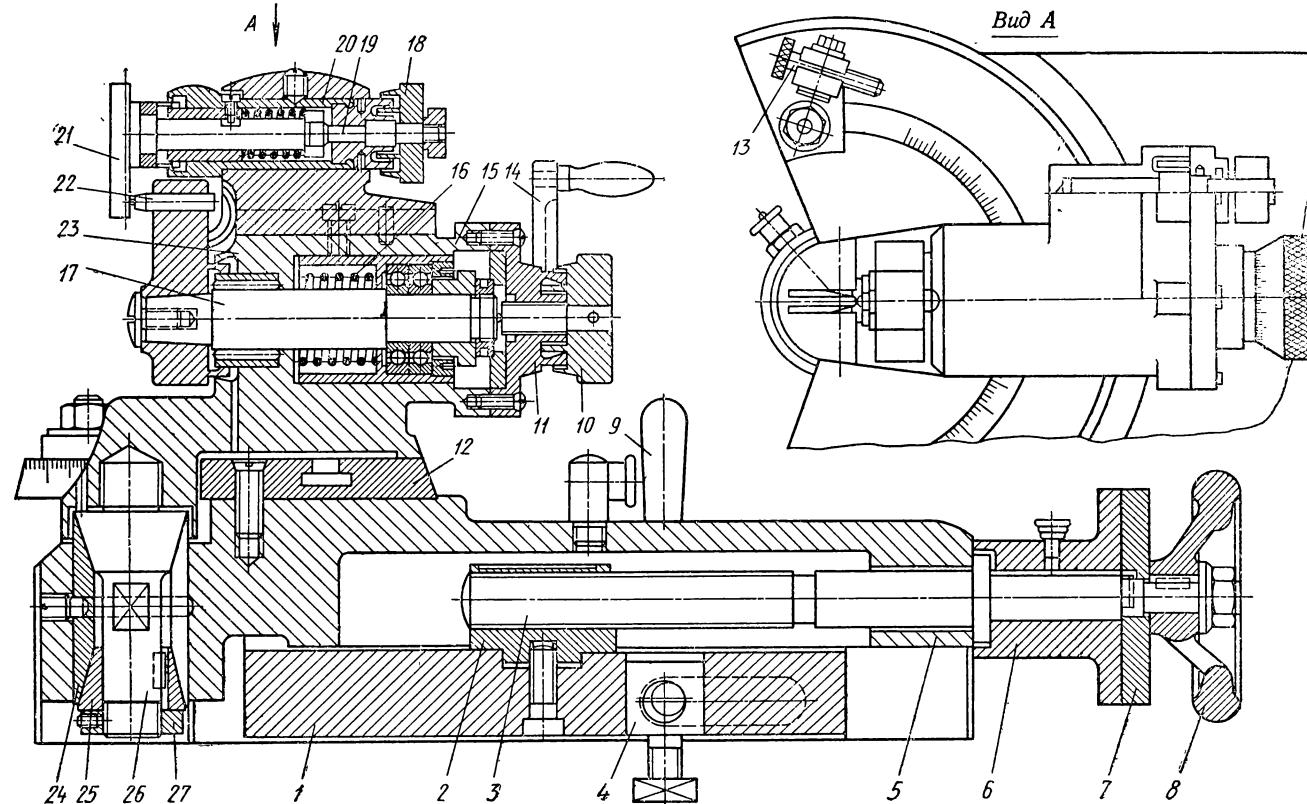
Приспособление к резьбошлифовальному станку для профилирования шлифовального круга
